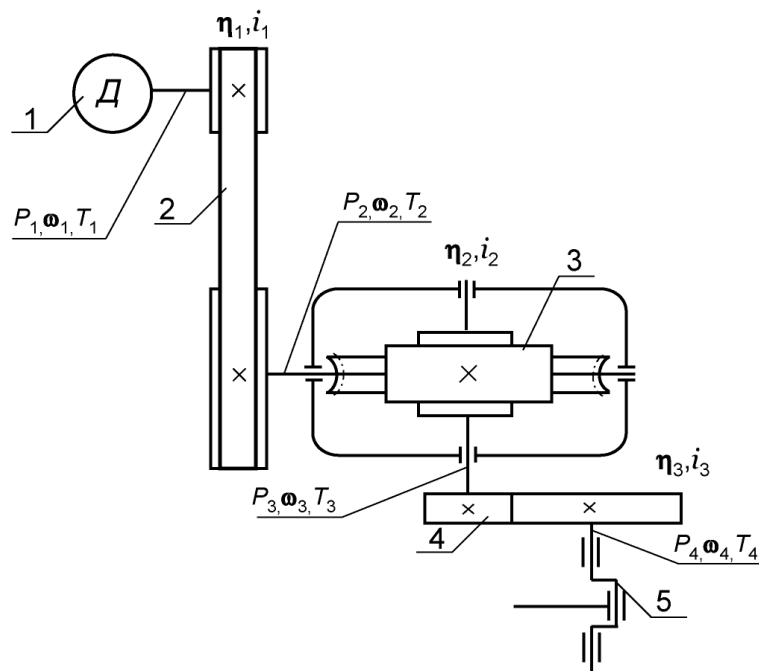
Кінематична схема приводу з черв'ячним редуктором:
